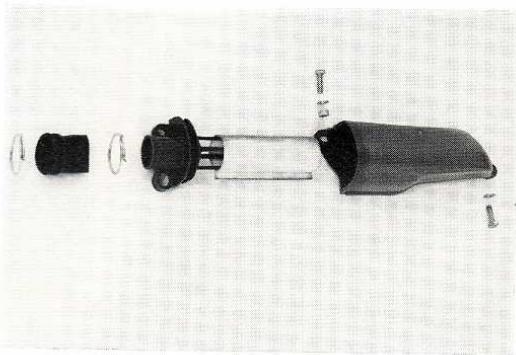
DEMONTAGE DU FILTRE A AIR.
